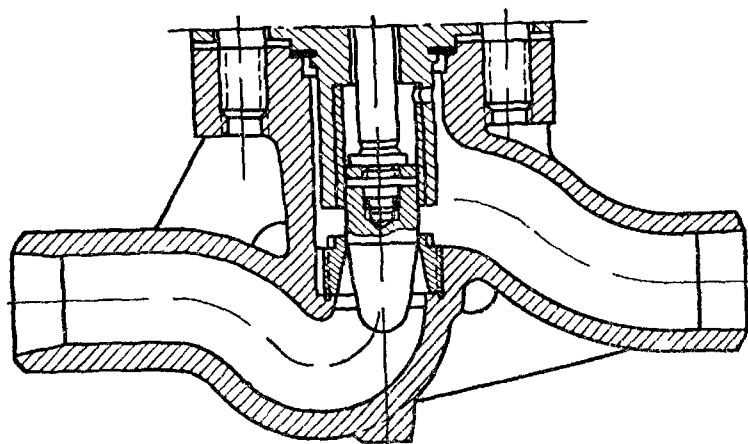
Регулирующий вентиль для воды ВАЗ.
